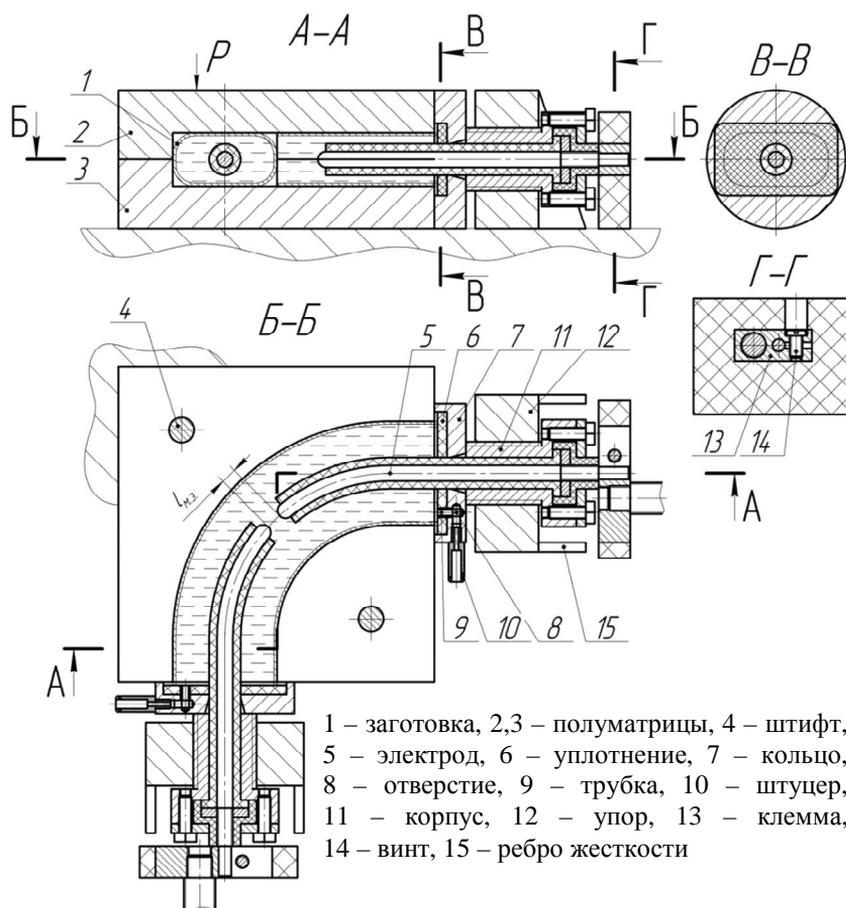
Конструкция модернизированного устройства для ЭГИ штамповки
